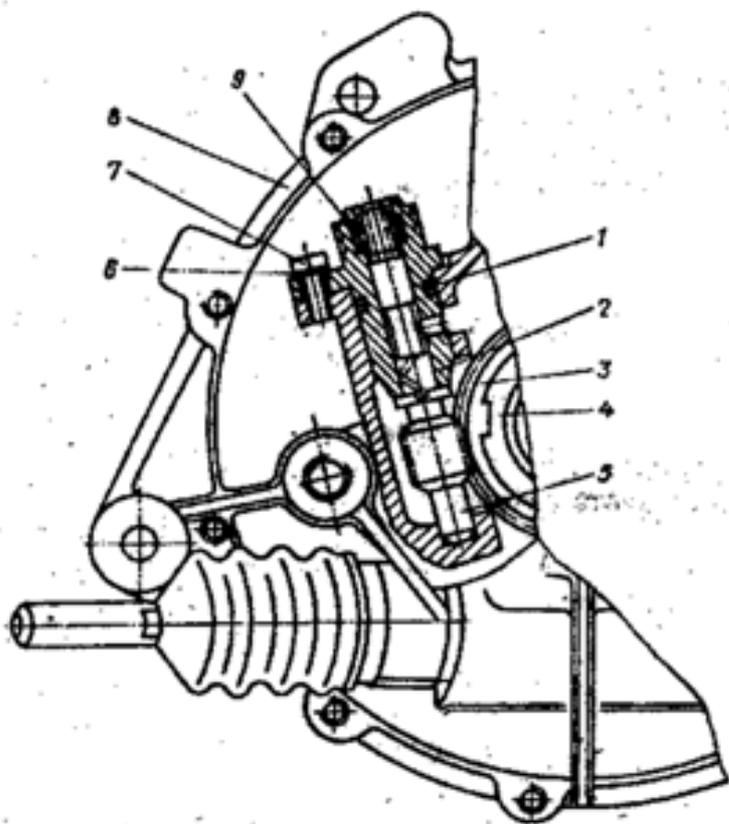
Привод спидометра: 1 - кольцо уплотнительное; 2 - корпус привода спидометра; 3 - ведущая шестерня; 4 - коробка дифференциала; 5 - вал-шестерня ведомая привода спидометра; 6 - шайба; 7 - болт; 8 - картер сцепления
